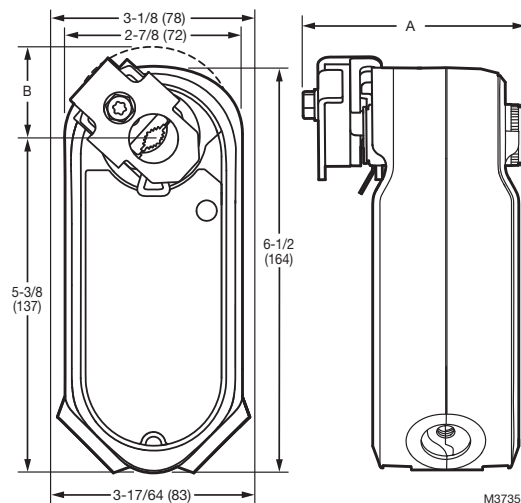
Габаритный чертеж исполнительного механизма без кабелепровода в дюймах (мм). Размеры А и В см. в табл. 2.
